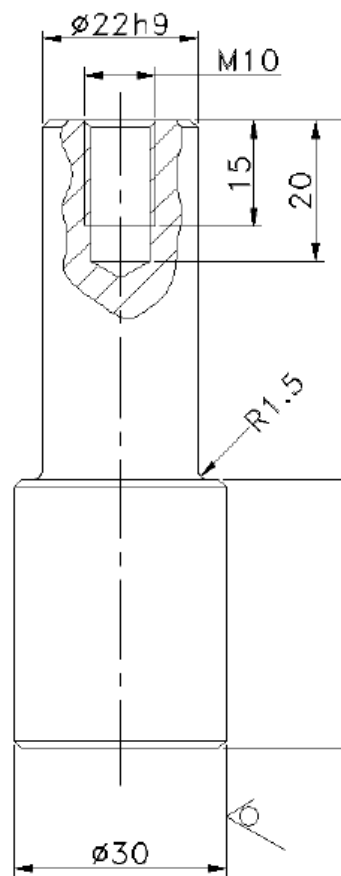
disegno tecnico del perno con quote,raggio di raccordo, tolleranze, filettatura.
